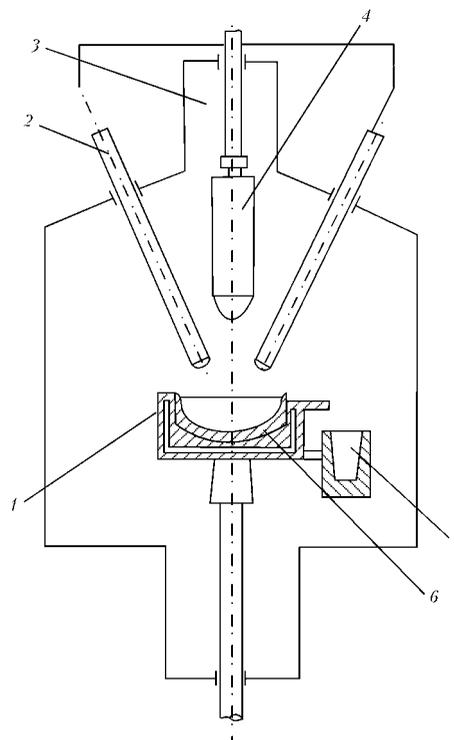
Схема плазменно-дугового переплава и литья в изложницу: 1 — медный водоохлаждаемый тигель; 2 — две пары плазмотронов постоянного тока; 3 — колонна с механизмом подачи расходимой заготовки; 4 — расходимая заготовка; 5 — изложница; 6 — гарнисажный слой, который образуется на поверхности холодного тигля в процессе плавления
